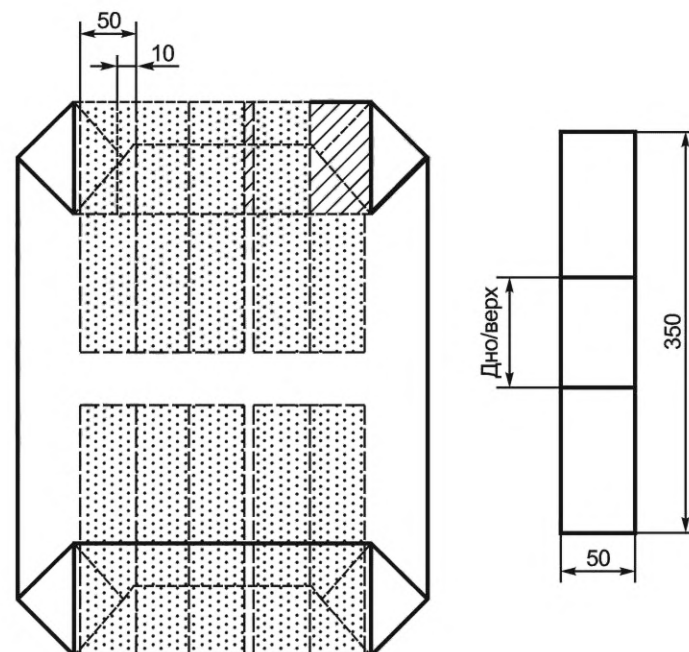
Схема подготовки образцов для контроля прочности термосваривания
